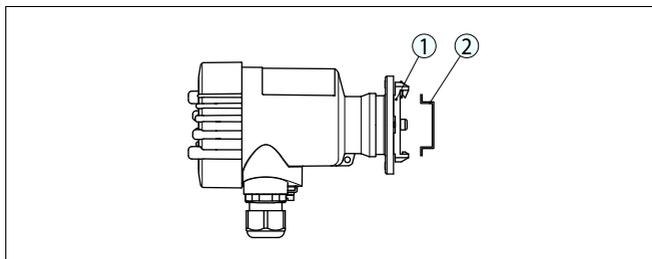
VEGADIS 61 для монтажа на несущей рейке
